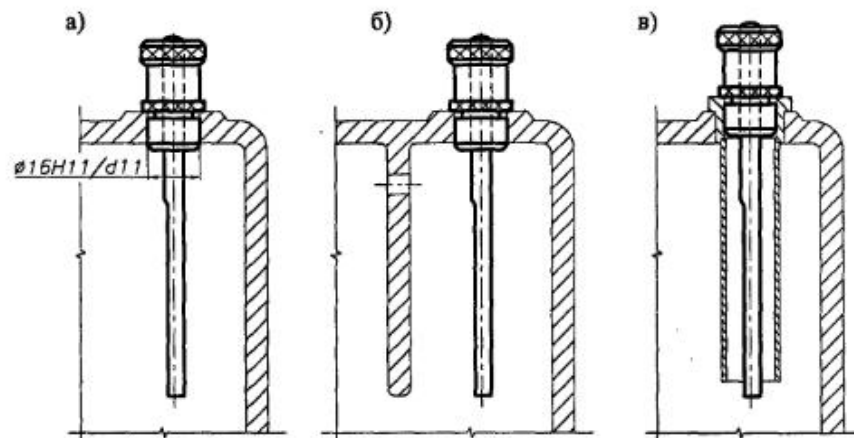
Установка жезлового маслоуказателя: а) непосредственно в корпусе; б) в камере корпуса; в) в чехле
